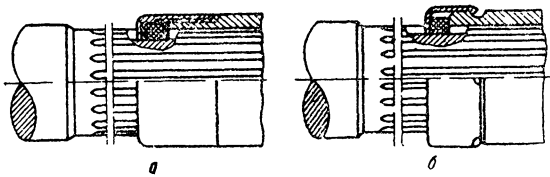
Сальниковое уплотнение подшипника опоры промежуточного карданного вала:
